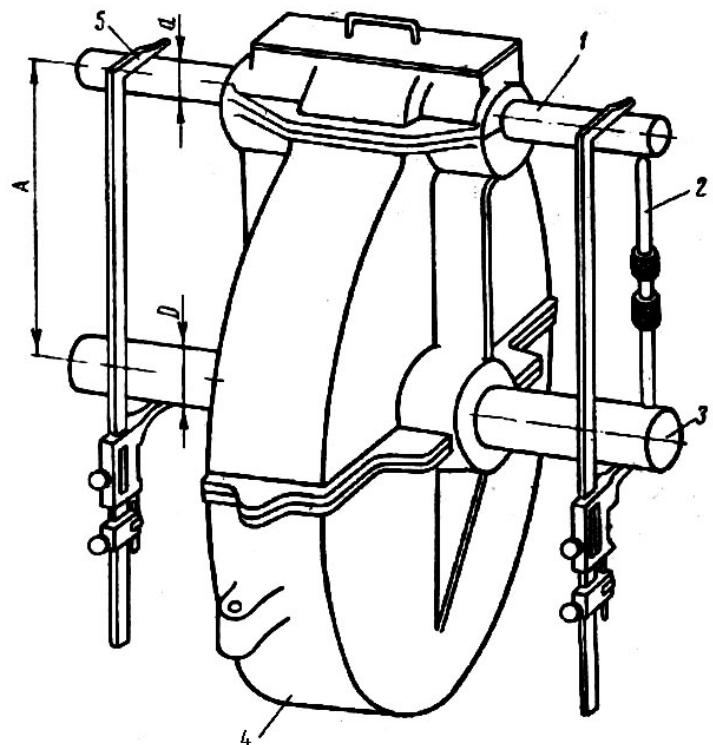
Проверка расстояния между осями цилиндрических зубчатых колес
